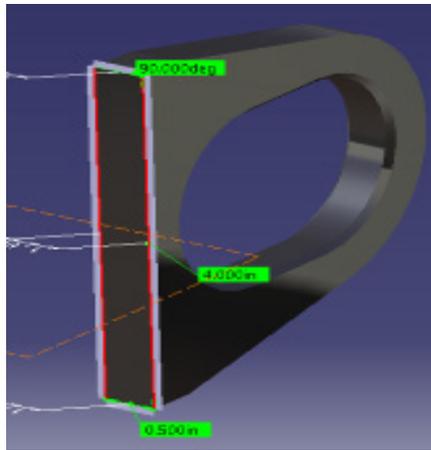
Longitud total de soldadura (L), para la oreja de carga.
